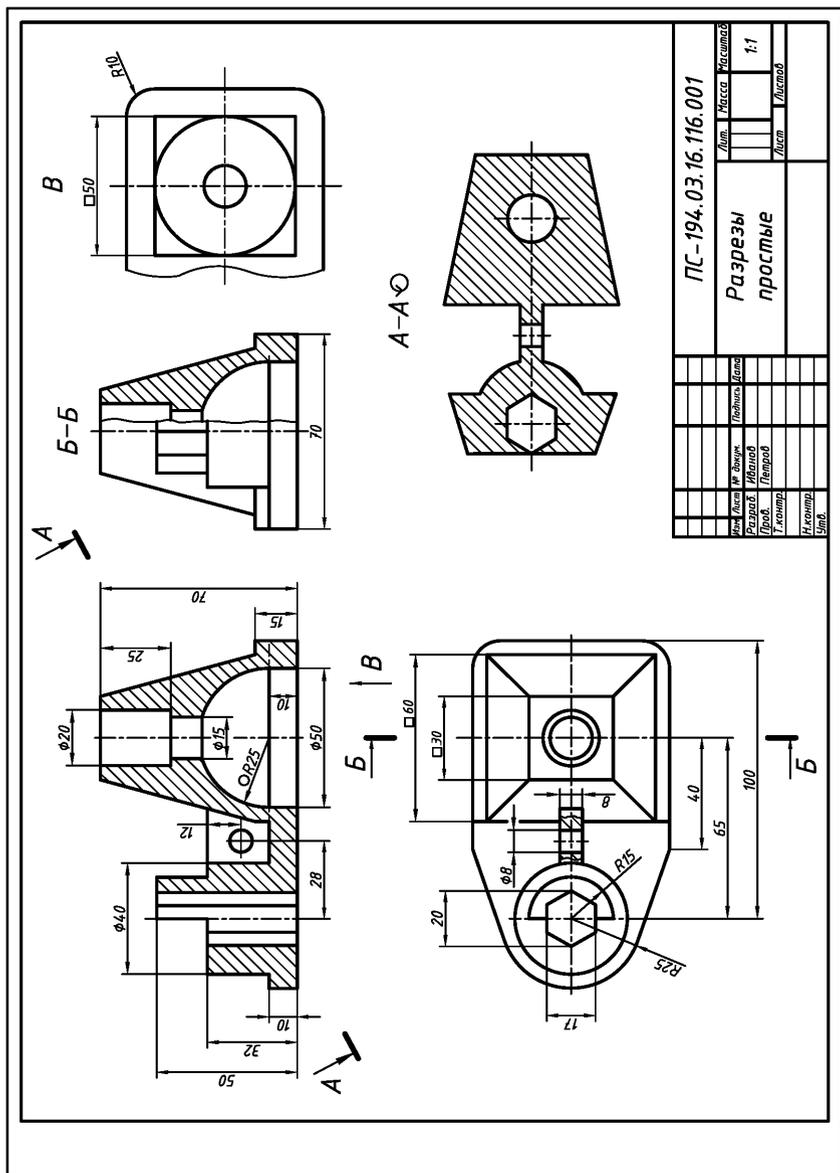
Пример оформления чертежа детали с одной плоскостью симметрии (вариант исходной заготовки – рис. 1.27)
